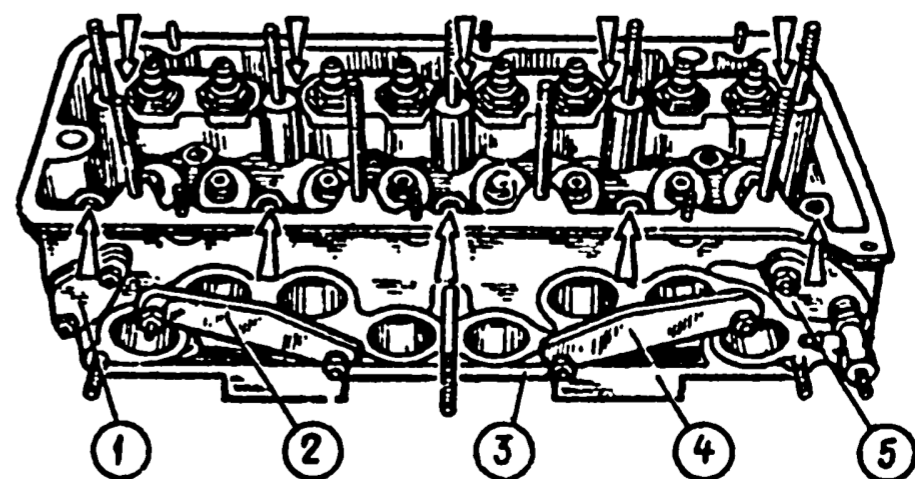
Проверка герметичности головки цилиндров на приспособлении А.60334: 1, 2, 4 - заглушки; 3 - плата приспособления; 5 - фланец со штуцером подвода воды
